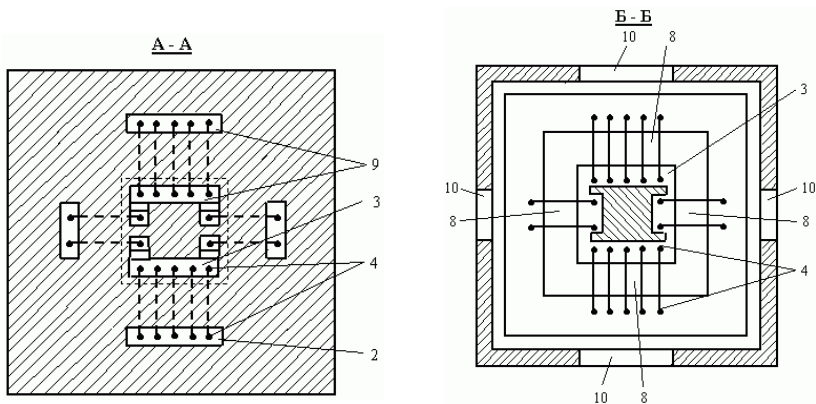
Схема расположения пазов над микросоединениями кристалла и корпуса
